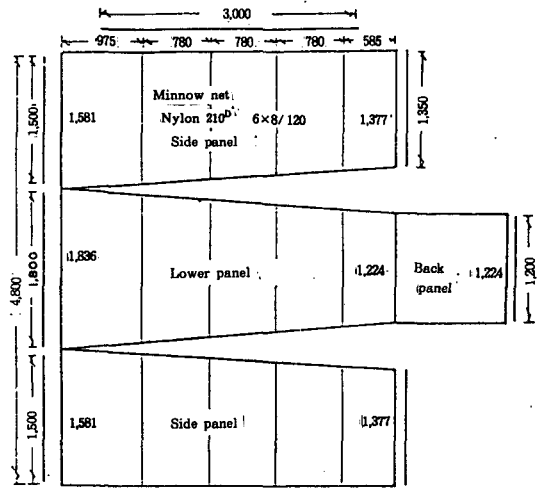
원통망지의 배치 (Scale, 1/10 : 단위 mm)
